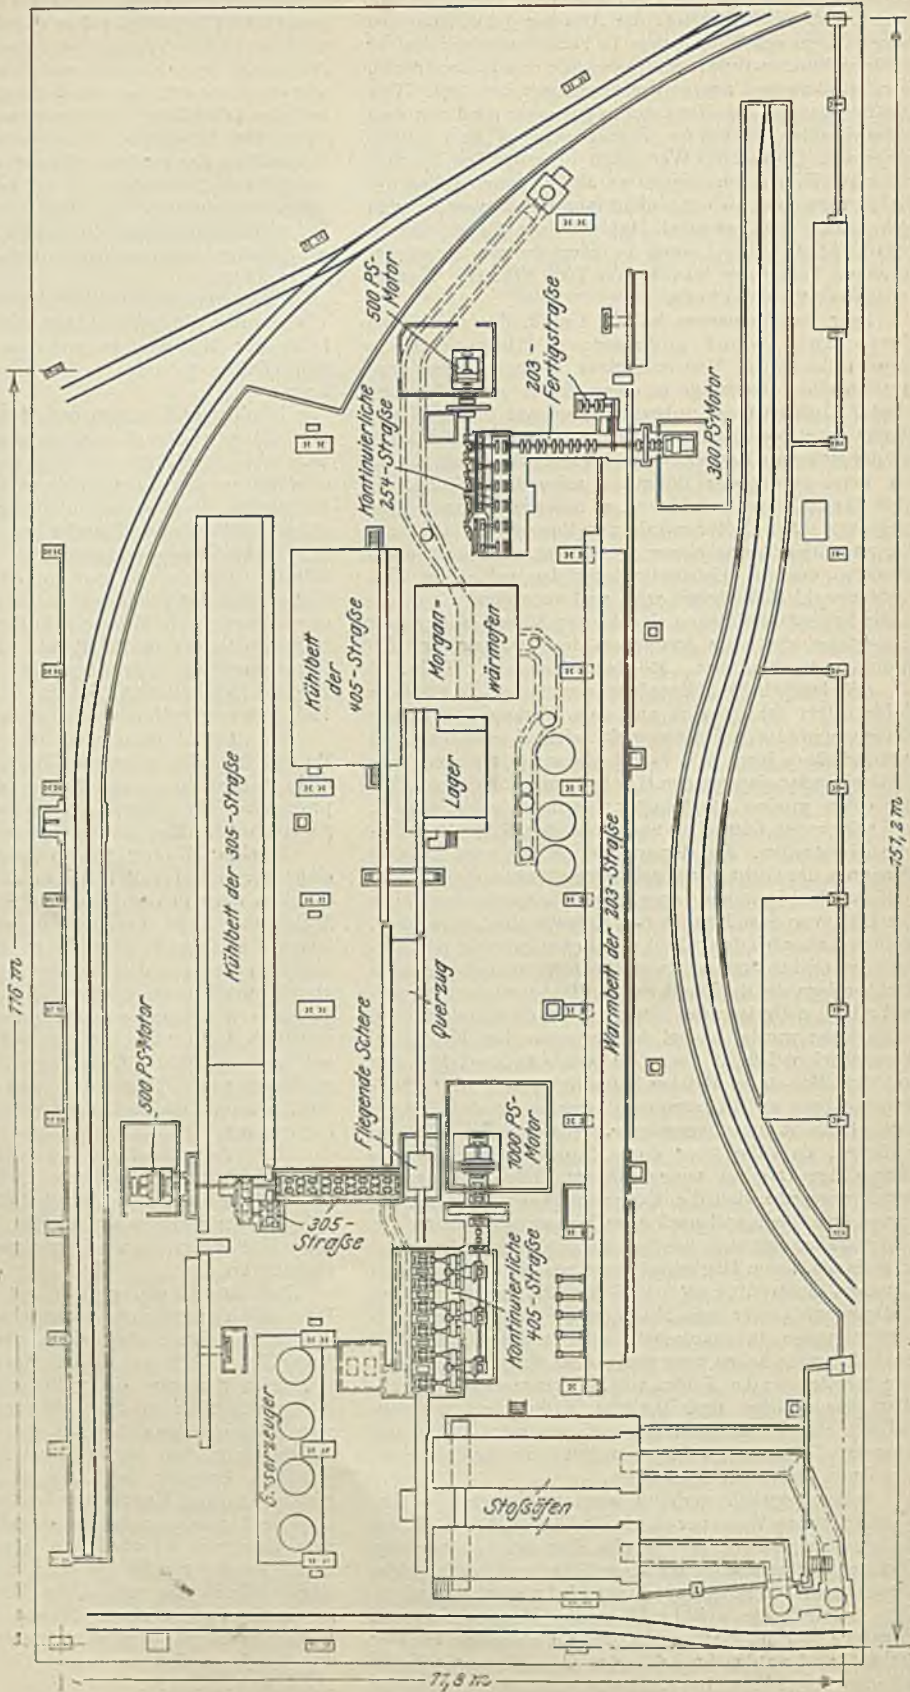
Stabeisenwalzwerk der Cambria Steel Co.
